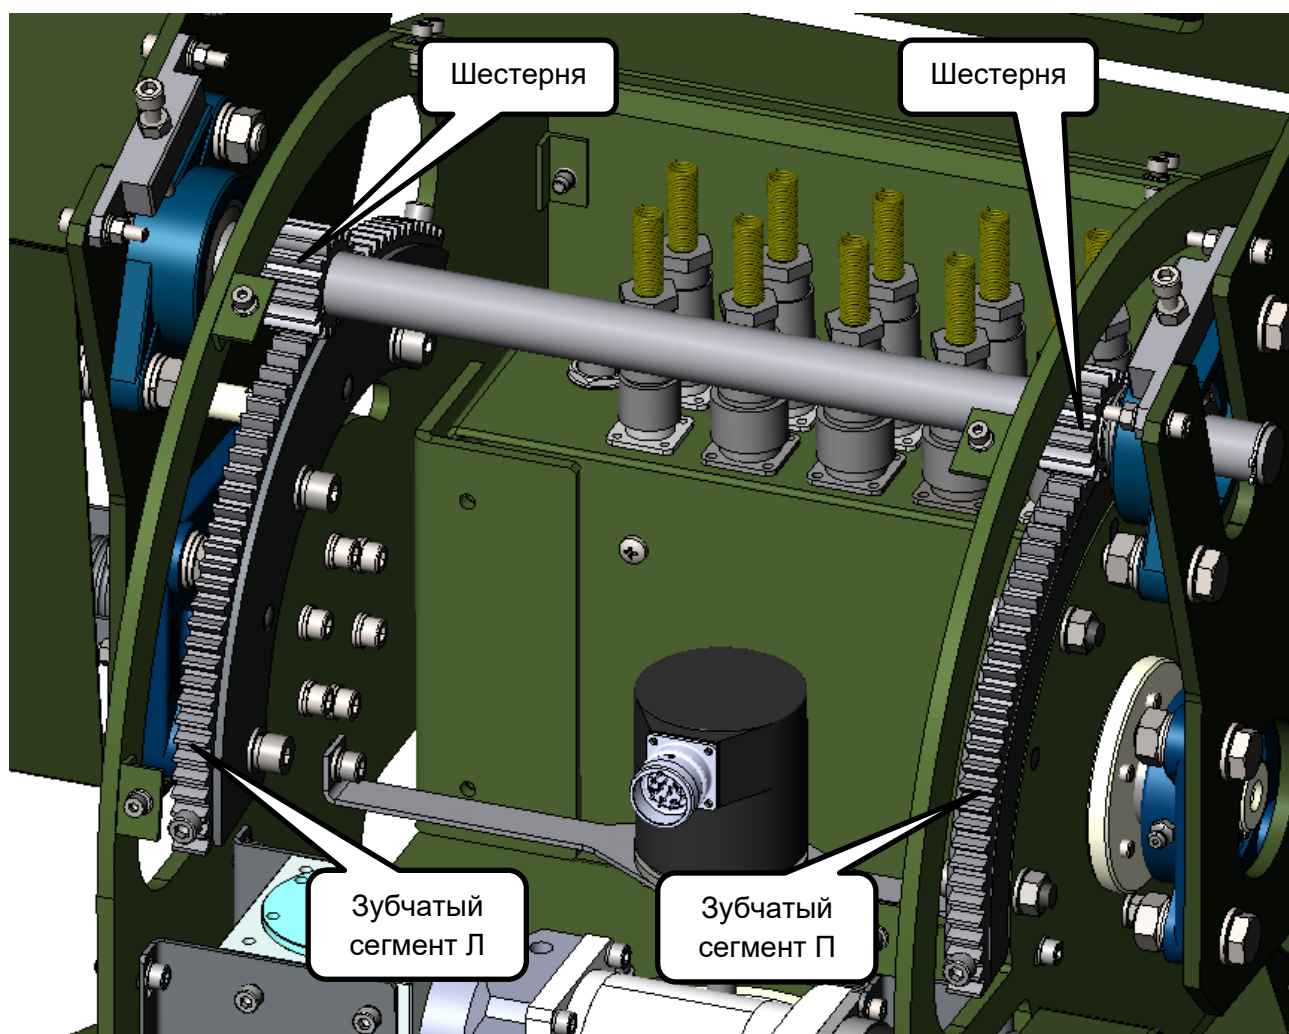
Внешний вид зубчатых сегментов и шестерен угломестного привода СССТ 1,2 м (защитный кожух не показан).
